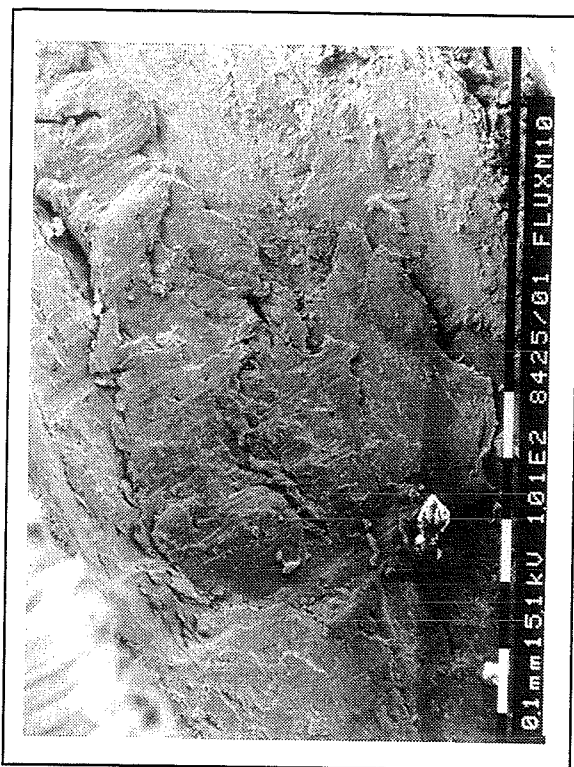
vervuiling in de contactbuis 100 X vergroot.
